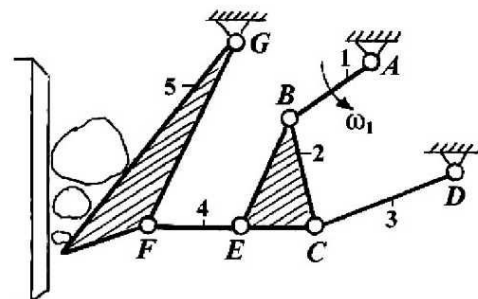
Механизм перемещения подвижной щеки дробилки
